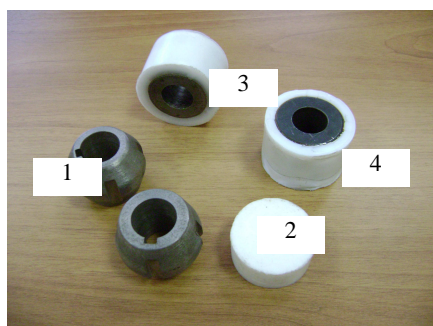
Металлополимерные подшипники скольжения с облицовкой из фторопласта-4, полученные объёмной штамповкой:
